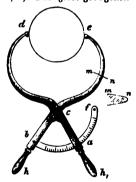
Baumzirlel. c Gewinde, hh' handhaben, baf Scala, l'Anjchlagzapfen. Rebenfigur Schnitt nach m n.
